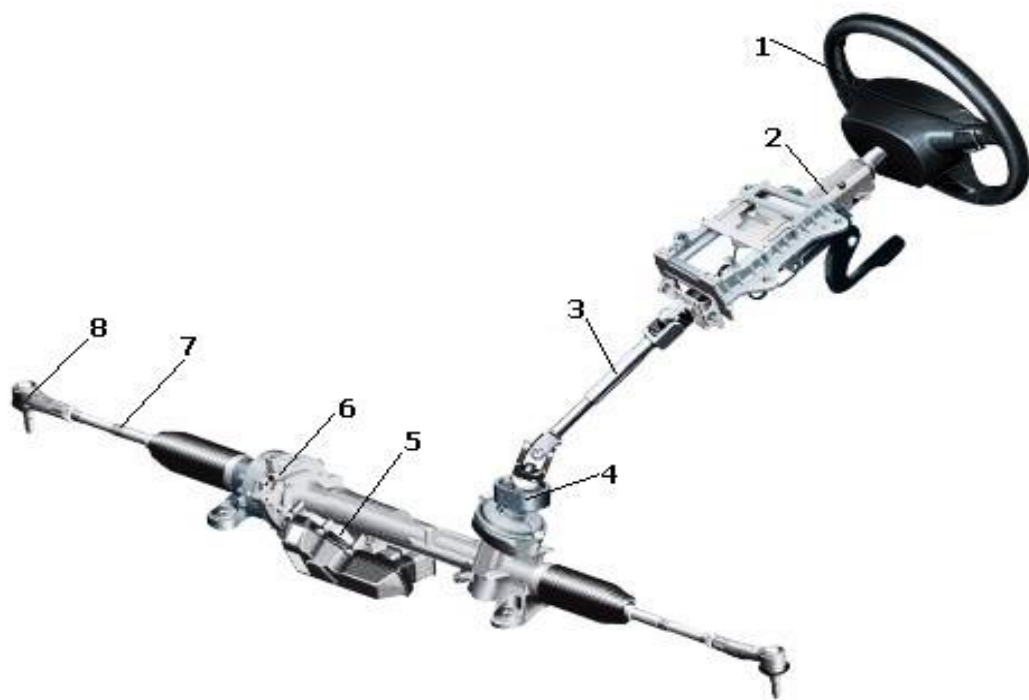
Общий вид рулевой механизм типа шестерня-рейка: 1 - рулевое колесо; 2 - рулевая колонка; 3 - карданный вал; 4 - датчик или золотниковое устройство крутящего момента на рулевом колесе; 5 - электроусилитель или гидроусилитель руля; 6 - рулевой механизм; 7 - рулевая тяга; 8 - наконечник рулевой тяги с шаровым шарниром.
